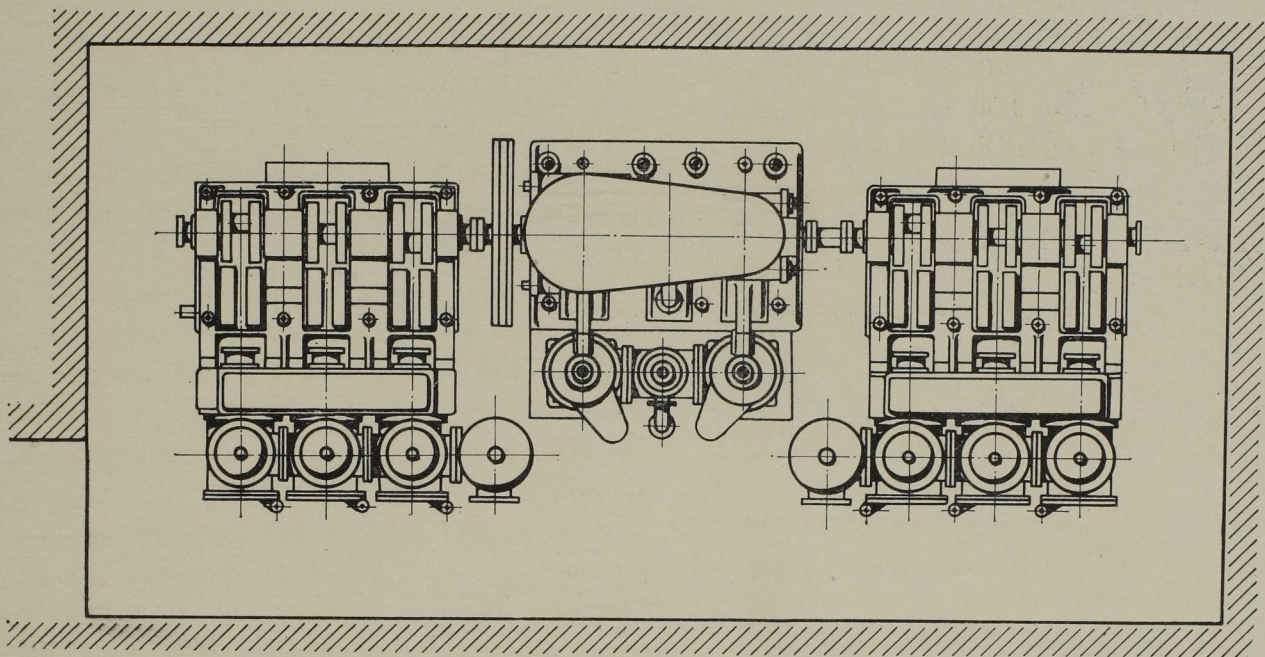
Grundriss der Pumpmaschine. Masst. 1:100.
